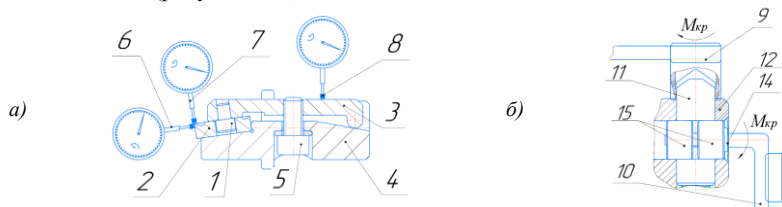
Конструктивные элементы сборных торцовых фрез
